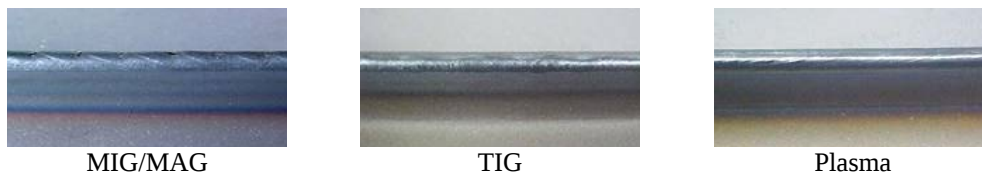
Aspecto típico dos cordões obtidos em função do processo de soldagem
